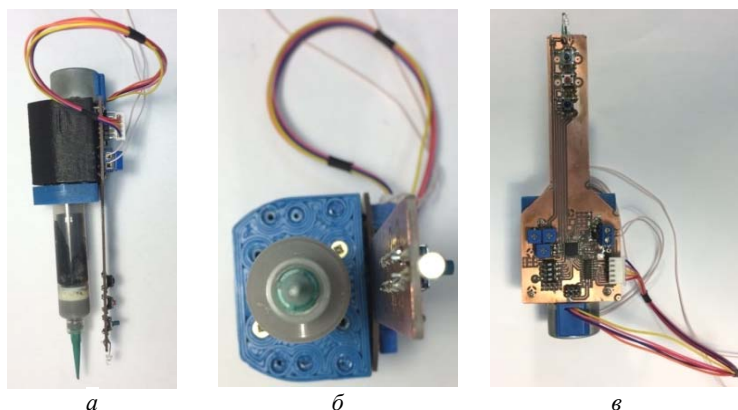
Дозатор паяльной пасты, выполненный с элементами трехмерной печати: *а* – вид сбоку; *б* – вид спереди; *в* – вид сверху
